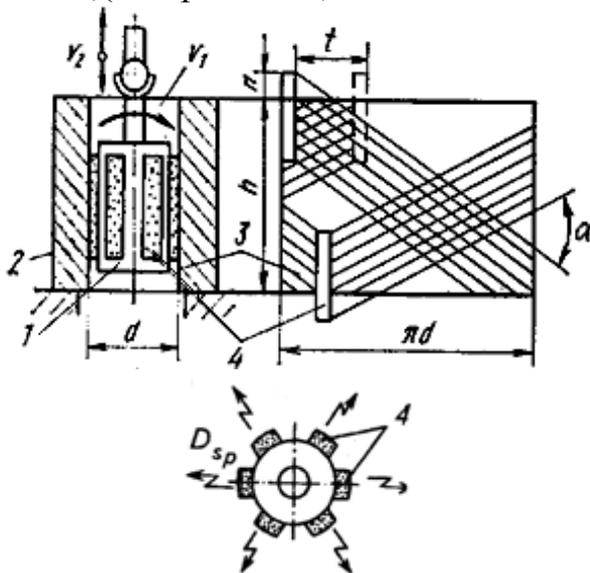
Схема хонингования отверстия: 1 – хонинговальная головка; 2 – обрабатываемая заготовка (втулка); 3 - внутренняя поверхность втулки; 4 - хоны
